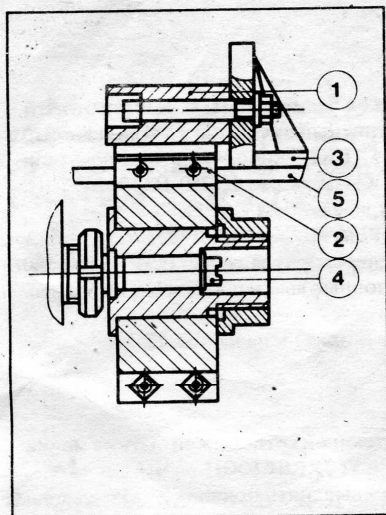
Фреза и колодка для выставления режущих пластин фрезы.
